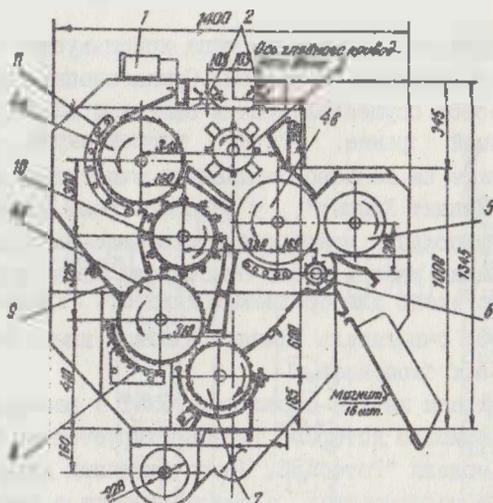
Питатель-очиститель валкового дмца модели "Макс-Флоу": 1 - привод питателя; 2 - питающие валики; 3 - колково-планчатый барабан; 4 - а, б, в - пальчатые барабаны; 5 - съемный пальчатый барабан; 6 - набрасывающий валик; 7 - регенерационный барабан; 8 - колосниковая решетка; 9 - поднимная сетка; 10 - съемный барабан; 11 - колосниковая решетка
